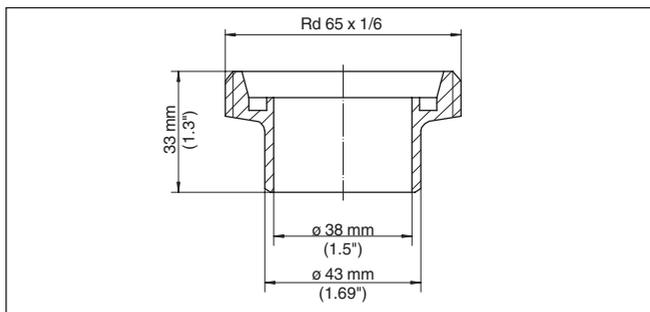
Medidas racor para soldar, racor roscado según DN 40 (DIN 11851)
